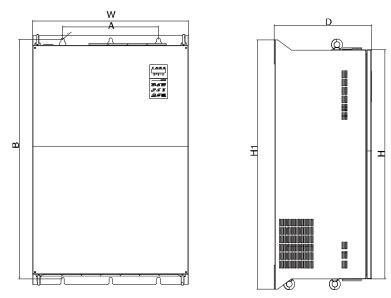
Схема внешних размеров и размеров монтажа металлической пластины 200G
